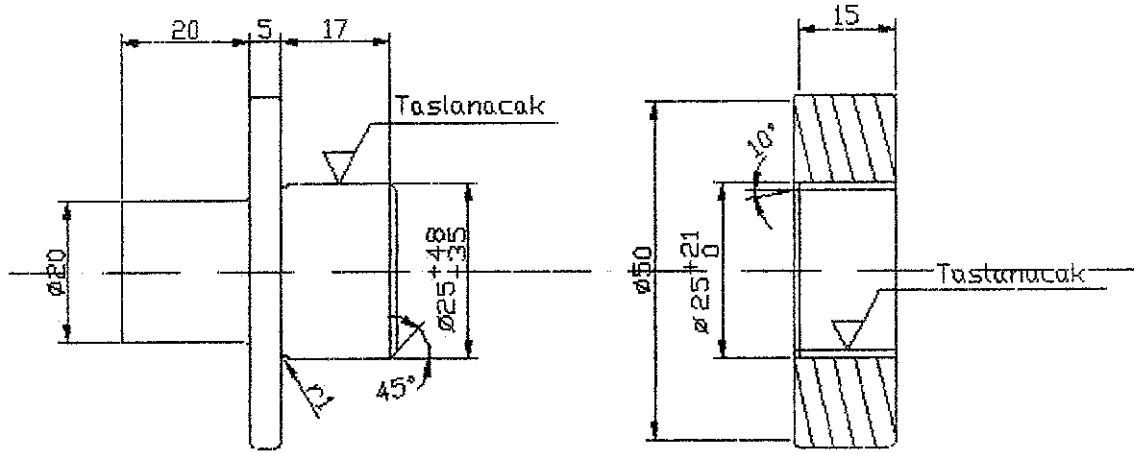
Millerin Yüzeylerinin Taşlanması, Mikrometre İle Ölçüm
